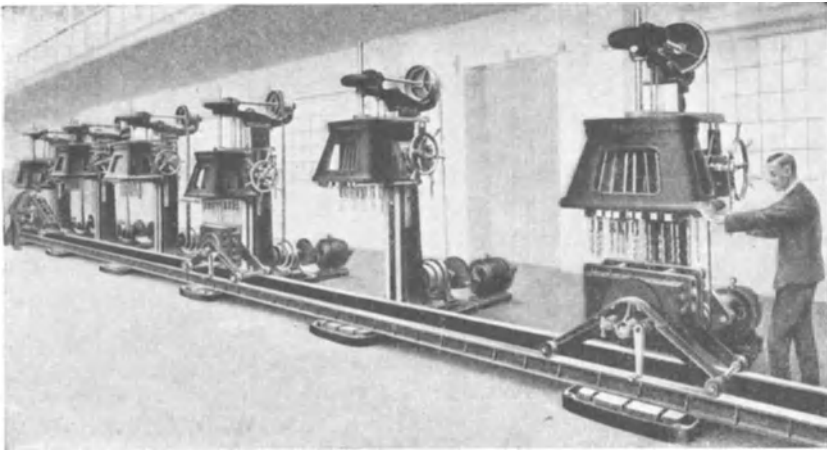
Bohrmaschinenstraße mit Einzelantrieb.
